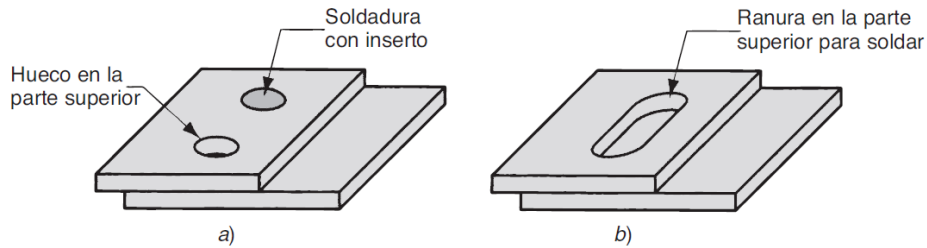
(a) Soldadura con inserto y (b) Soldadura ranurada.
